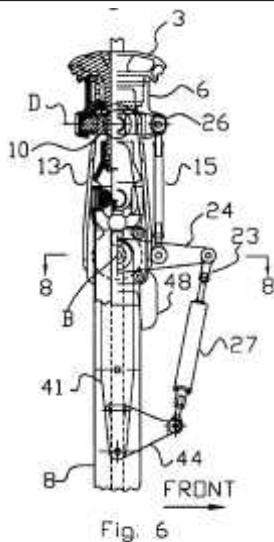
Vue de côté (partie gauche en coupe) de la tête rotor
